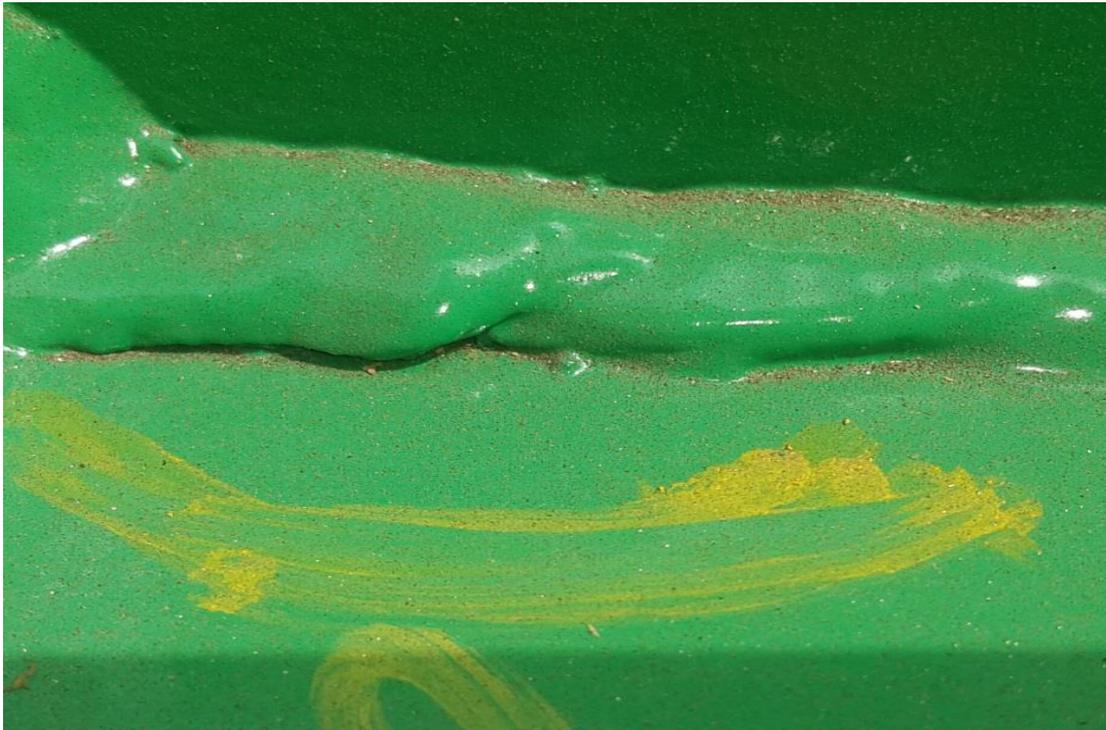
Código, HTD-S AUX-ER101_1 (Enrejado), defecto de soldadura OVERLAP
